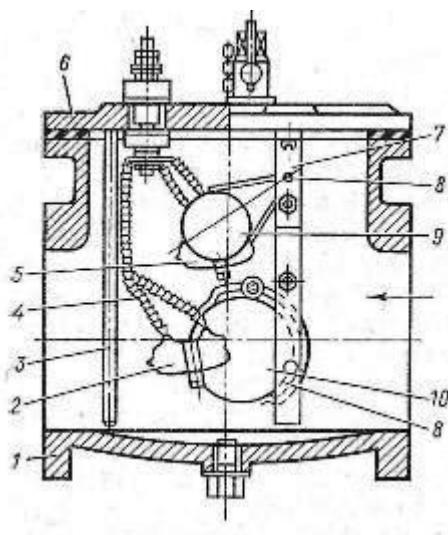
Газовое реле поплавкового типа: 1 - корпус, 2,5 - контакты, 3 - стержень, 4 - изоляция выводов, 6 - крышка, 7 - рамка, 8 - ось, 9 - верхний поплавок, 10 - нижний поплавок.
